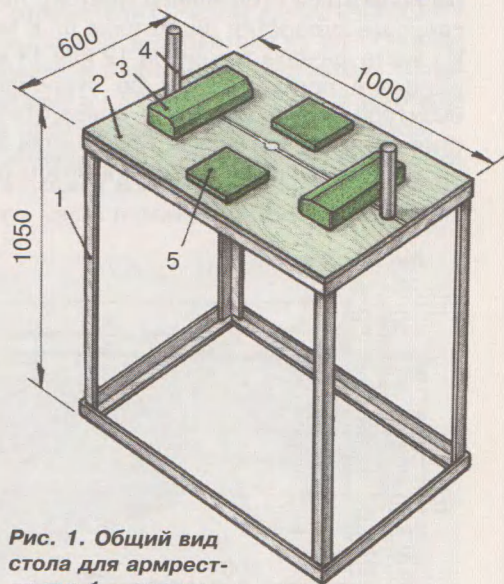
Общий вид стола для армрестлинга: 1 — каркас стола; 2 — щиток; 3 — валик; 4 — рукоятка; 5 — подлокотник.
